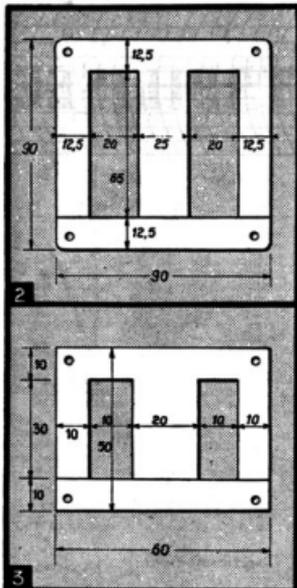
Aspect et dimensions d'une tube au silicium de modèle courant
